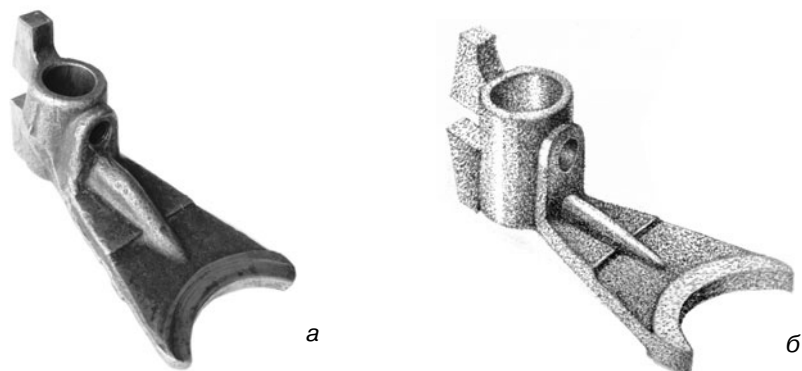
Рисование деталей с литыми поверхностями: а) фотография детали;
